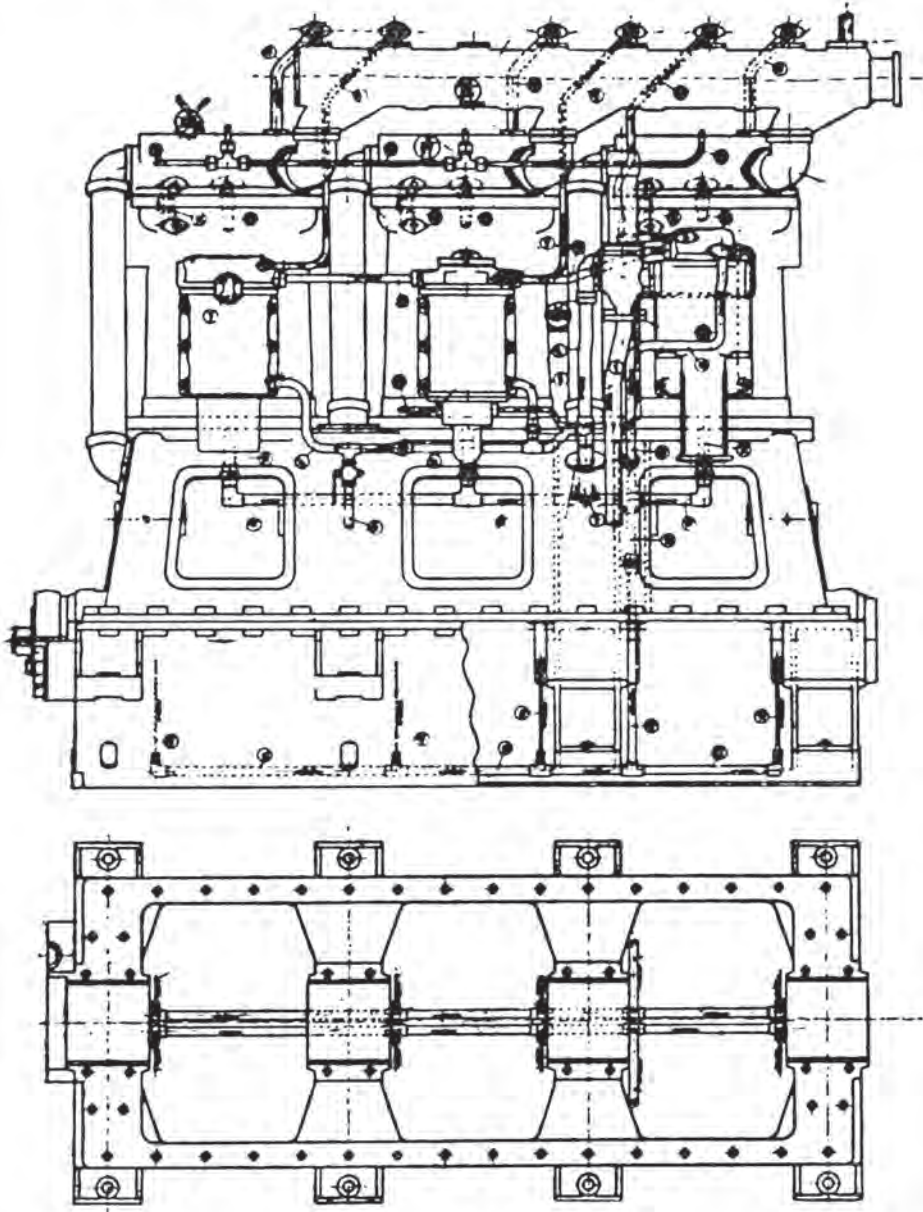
Поперечный разрѣзъ двигателя Дизеля.
